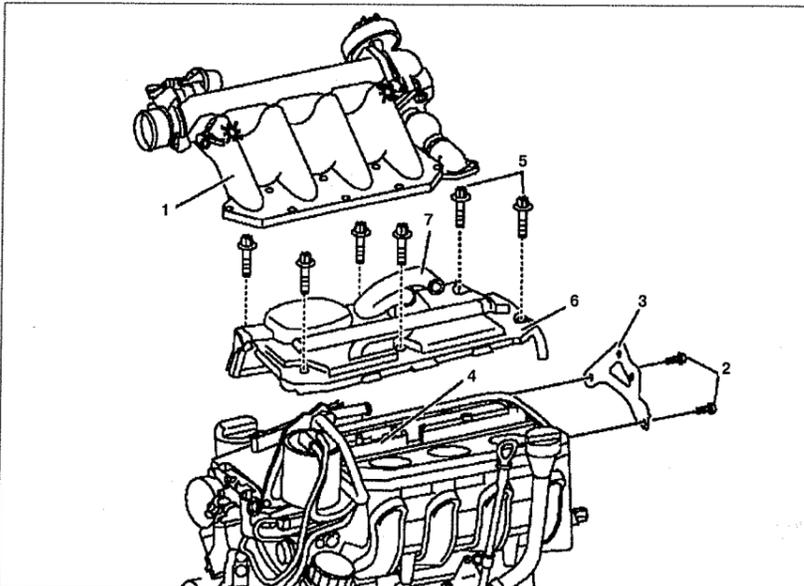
Декоративная панель крышки головки блока цилиндров:
